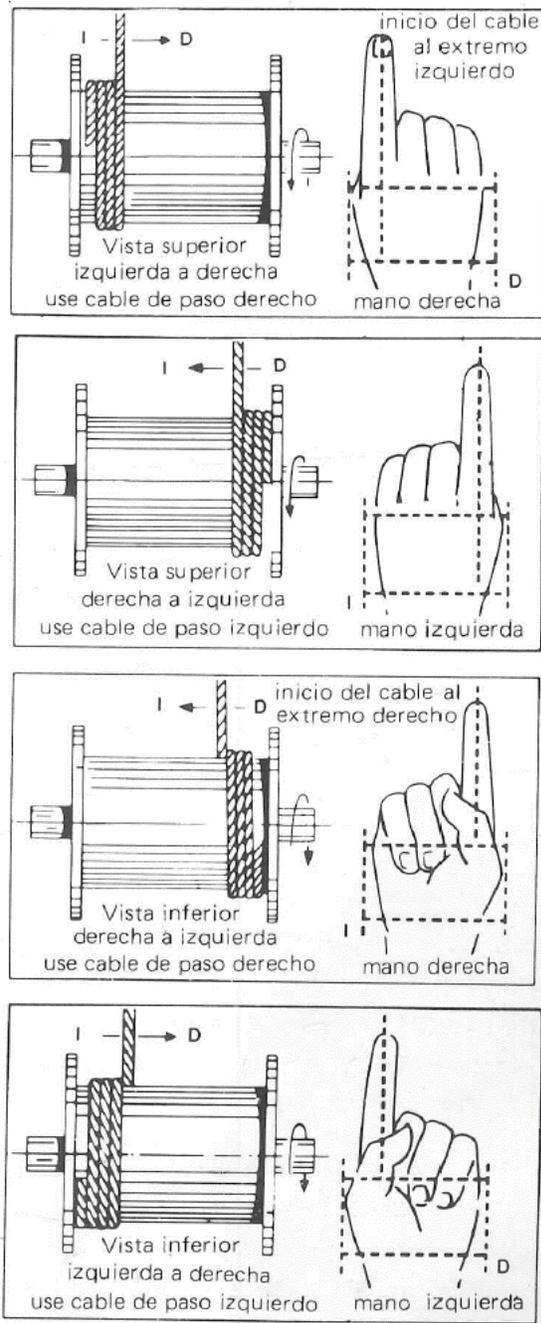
Regla práctica para el enrollamiento de cables con torsión izquierda o derecha [18]
